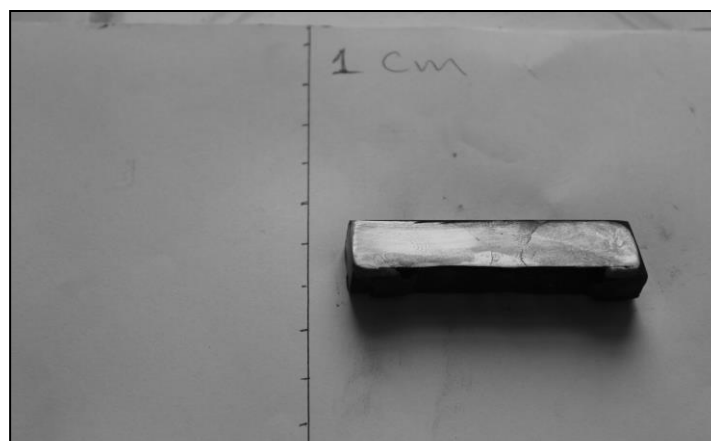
aspect macroscopique de l'acier et son joint soudé sans produits de corrosion.
